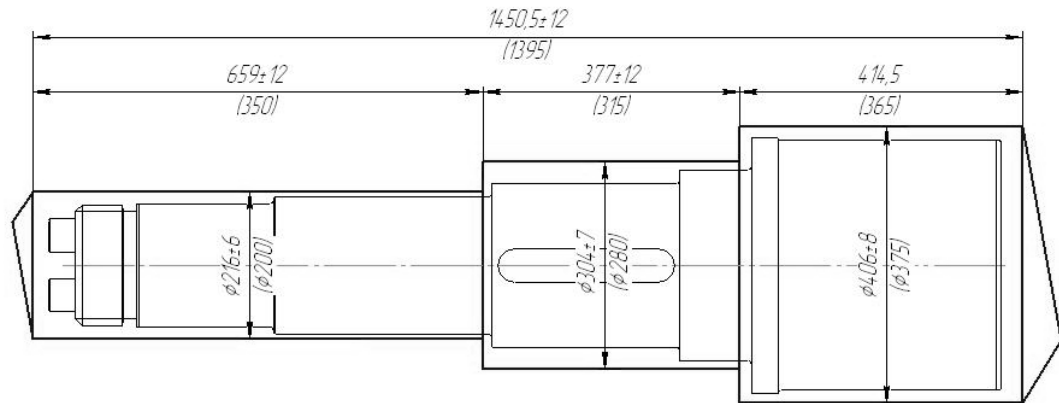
Заготовка поковка виготовлена ковкою на пресах
